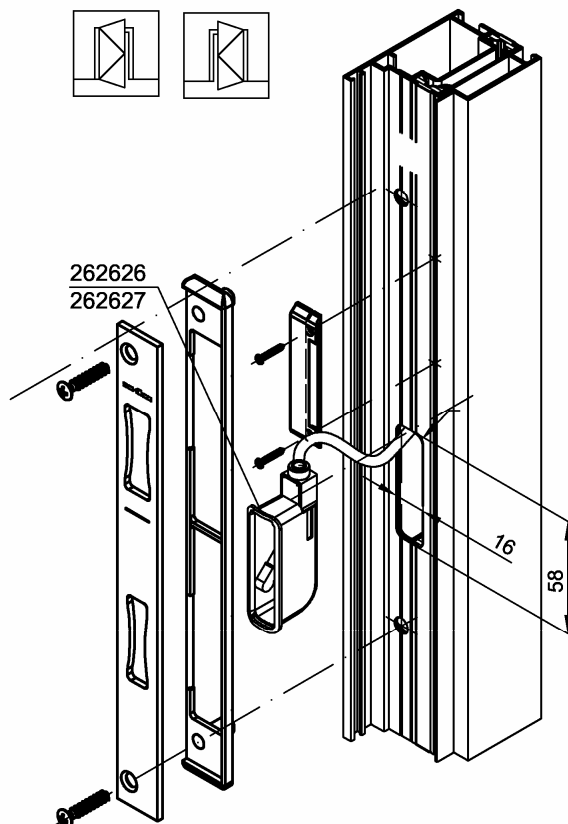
Montage Riegelschaltkontakt unter dem Schließblech, am Beispiel einer Tür ohne E-Öffner. Mit E-Öffner kann das Maß 58 mm größer sein.
